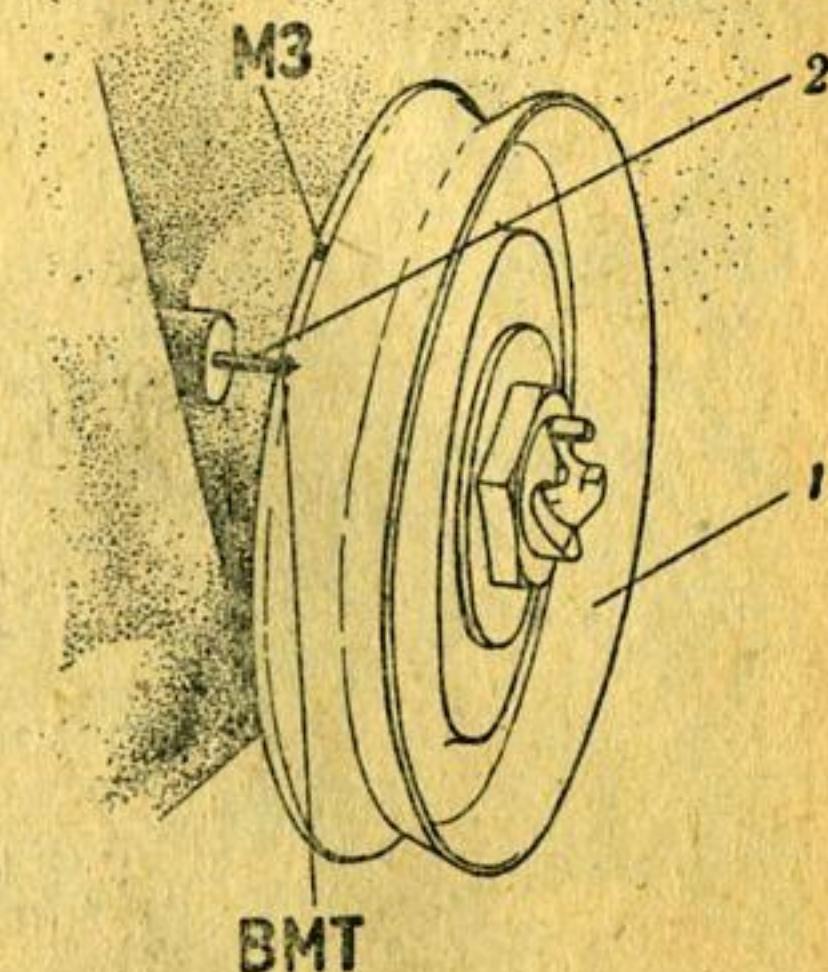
Установочные метки на ободе приводного шкива вентилятора:
